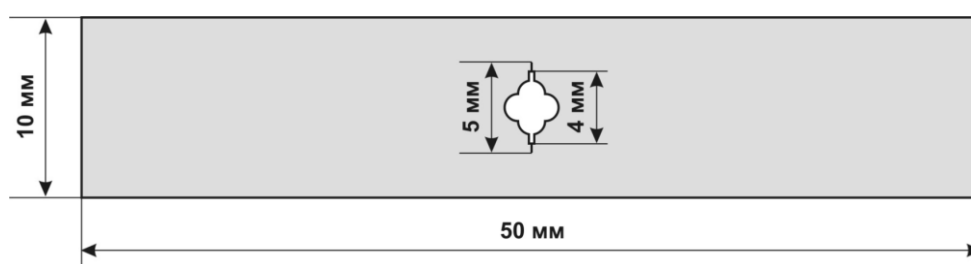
Образец с надрезом для испытания на статическое растяжение
